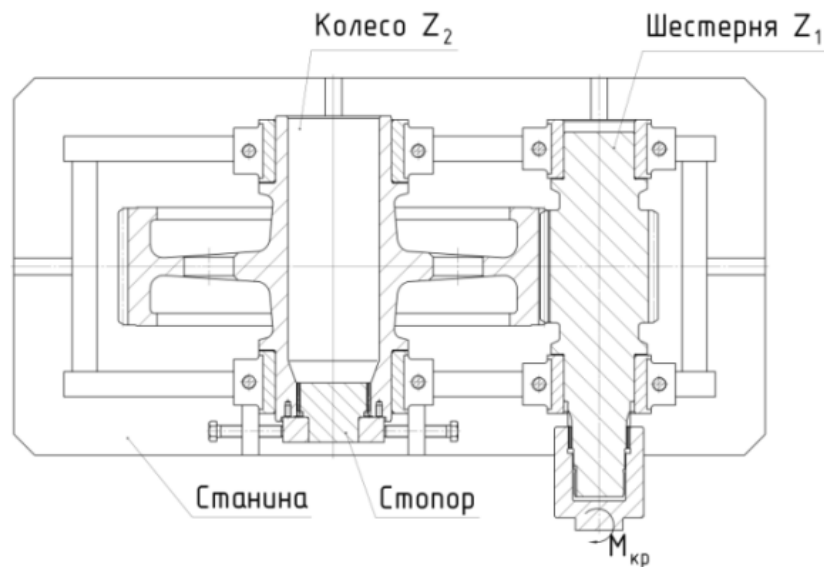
Принципиальная схема установка статического нагружения шестерни z_1 и колеса z_2 первой ступени опытного энергетического редуктора.
